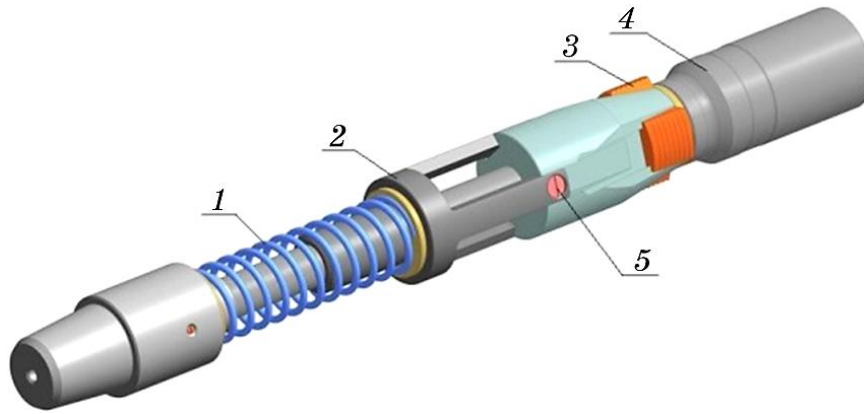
Захоплювач з механічною труборізкою: 1 — пружина, 2 — штовхач, 3 — плашка, 4 — вал, 5 — гвинт.
